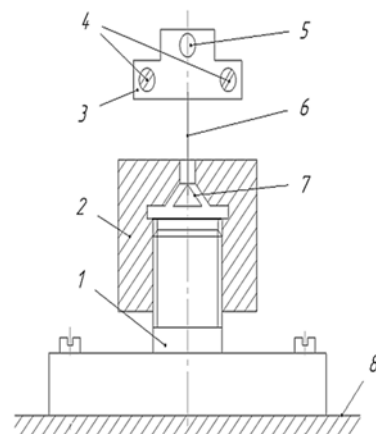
Конструкция приспособления для закрепления испытуемой иглы
